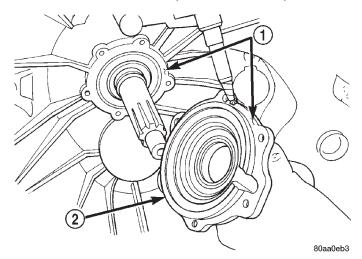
JUNTA DE RETENEDOR DE COJINETE Y CUBIERTA
